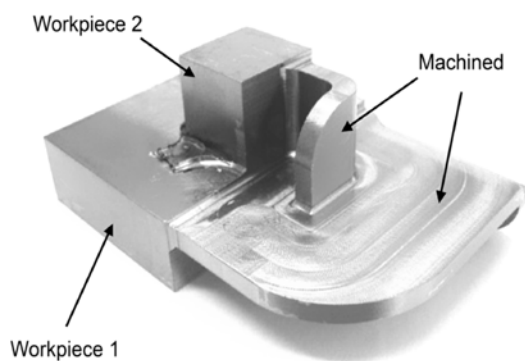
Изготовление заготовки путем ЛСТ с последующей механической обработкой [4]
